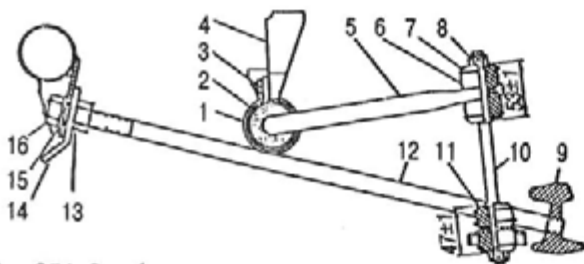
Стабилизатор и растяжка к передней подвеске: 1 - обойма; 2 - резиновая втулка; 3 - болт с гайкой; 4 - кронштейн; 5 - штанга; 6 - верхняя резиновая подушка; 7 - чашка; 8 и 16 - гайка; 9 - поперечина подвески; 10 - стойка; 11 - нижняя резиновая подушка; 12 - растяжка; 13 - контргайка; 14 - транспортировочная скоба; 15 - шайба
